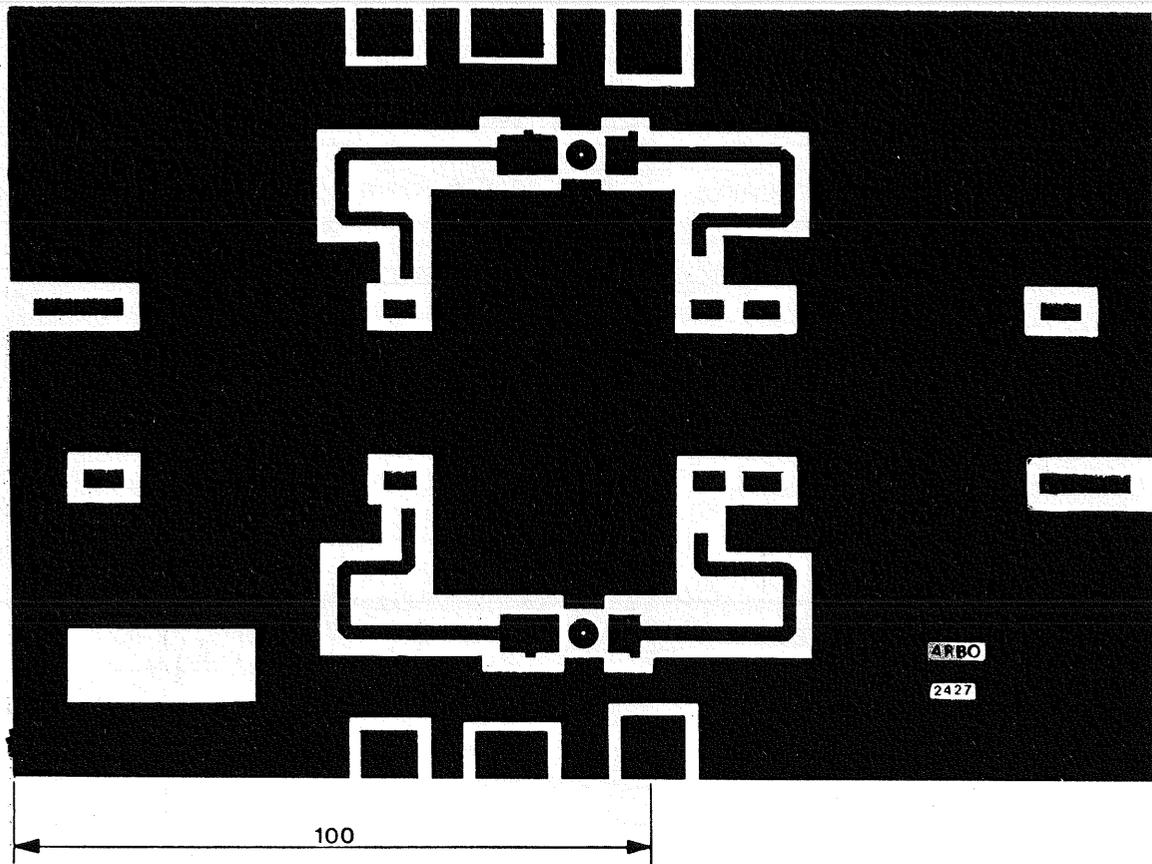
Dimensioni della piastra del circuito stampato vista dalla parte dove andranno montati i componenti; dimensioni 1 : 1
